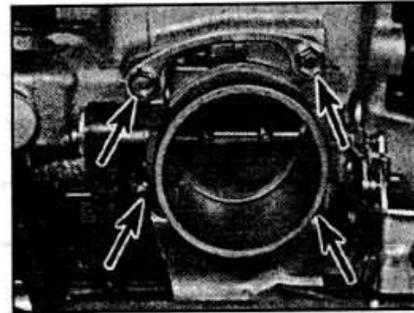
С.6. Расположение болтов крепления корпуса дросселей.
